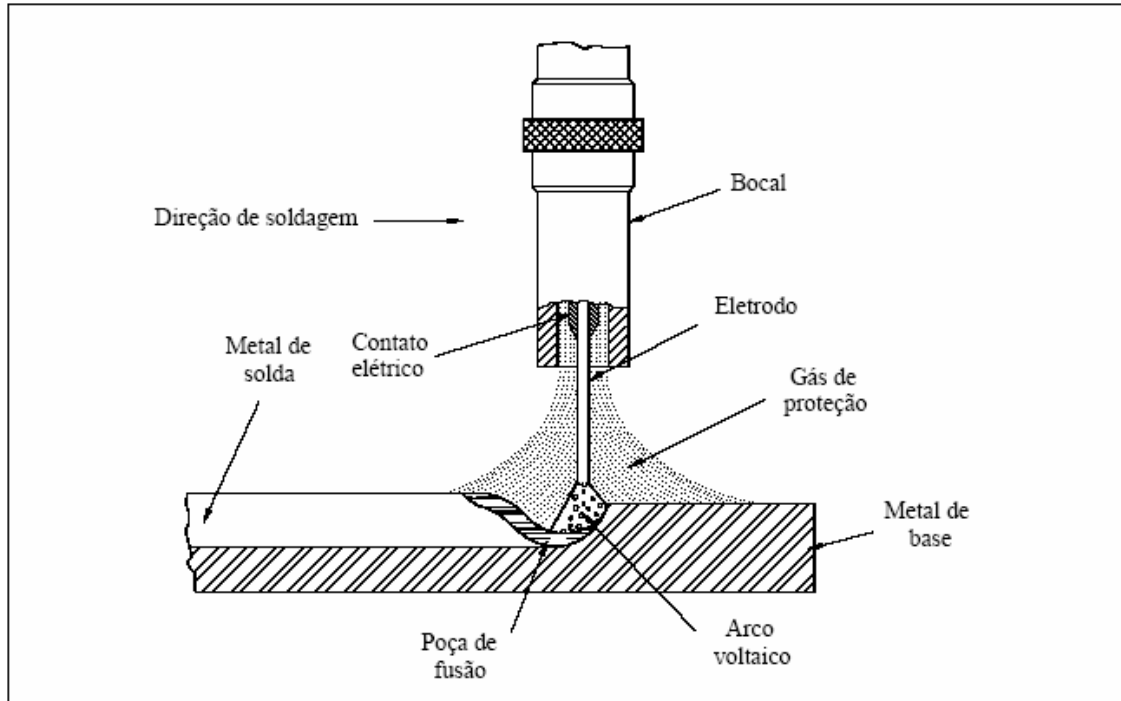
Detalhe da soldagem MIG/MAG (MIRANDA, 1999)
